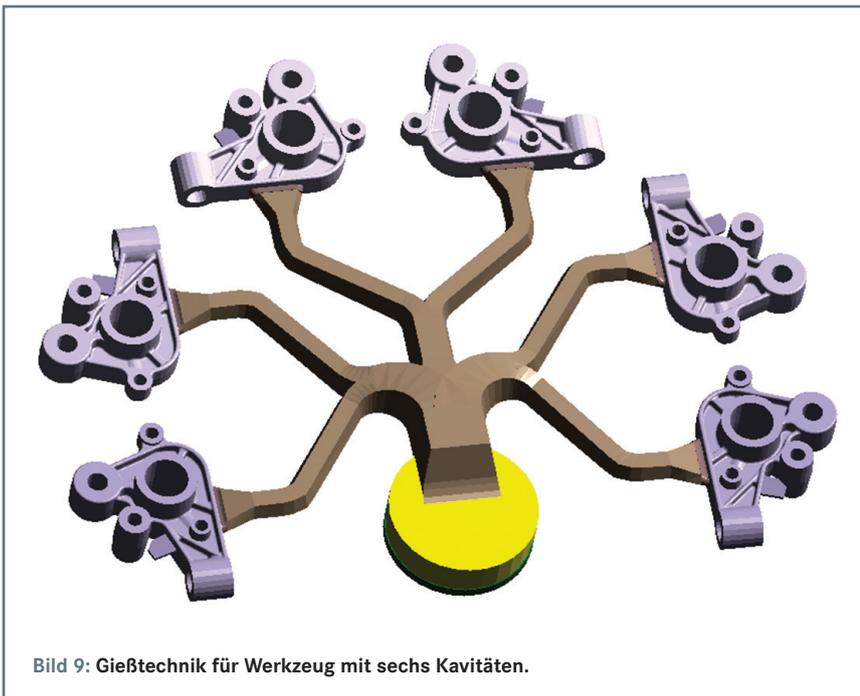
Gießtechnik für Werkzeug mit sechs Kavitäten.
